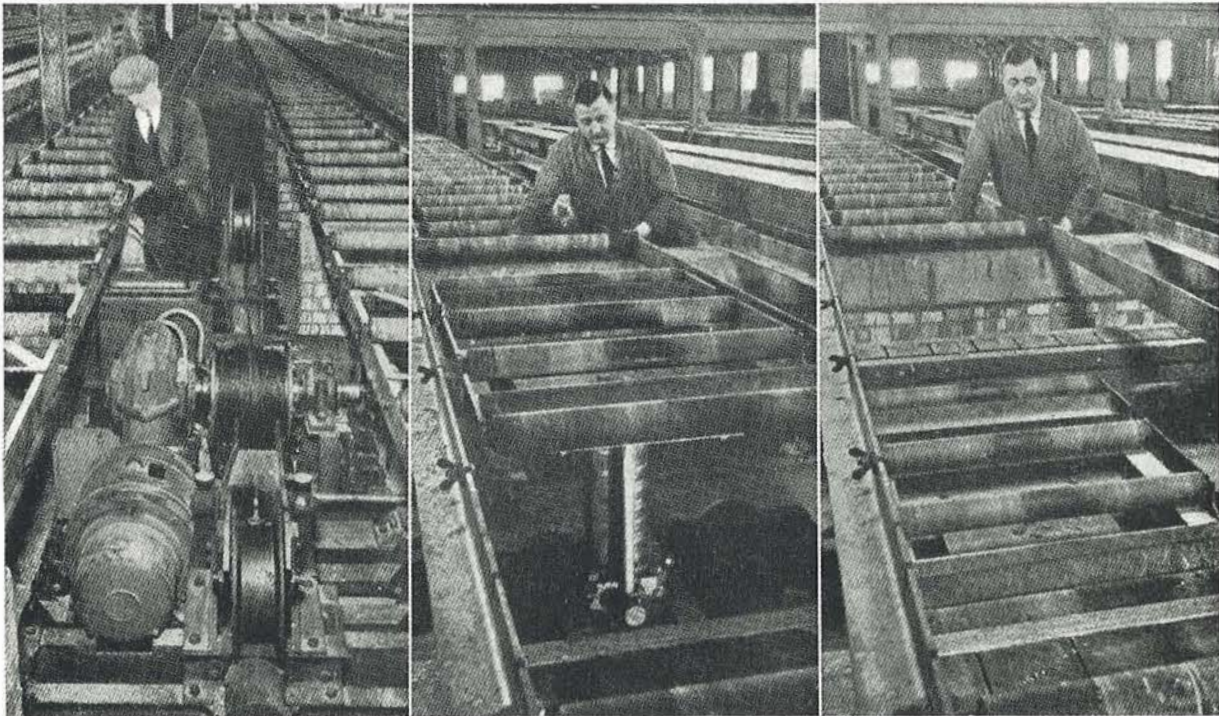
Cabrestante para mover las traviesas y elevador neumático para su traslado al transportador transversal.
